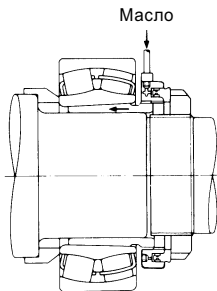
Посадка подшипника с помощью гидрогайки
